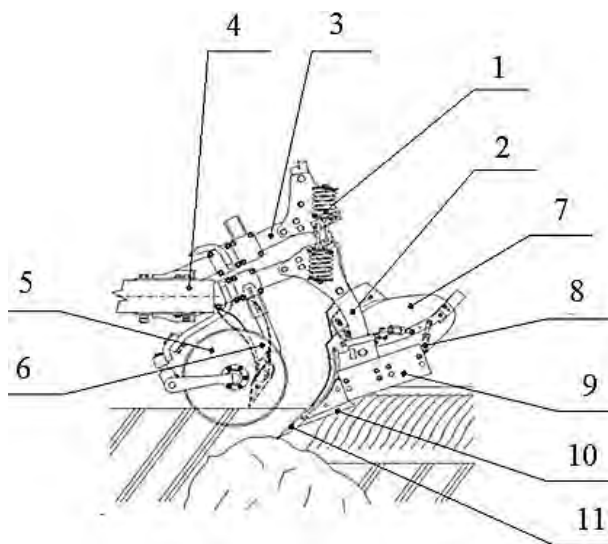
Корпус плуга с рычажно-пружинными предохранителями LEMKEN VARIOPAL 7X 4+1:
